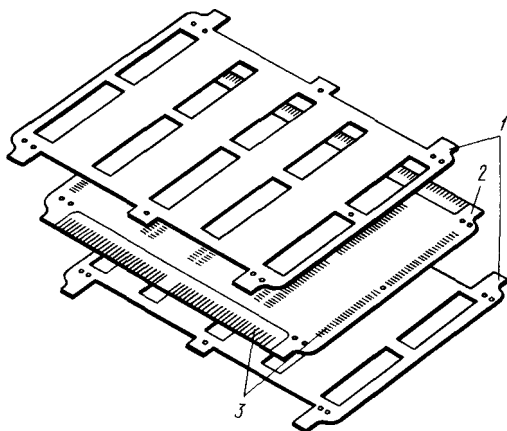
Конструкция ячейки с теплопроводящими шинами, расположенными с двух сторон печатной платы:
